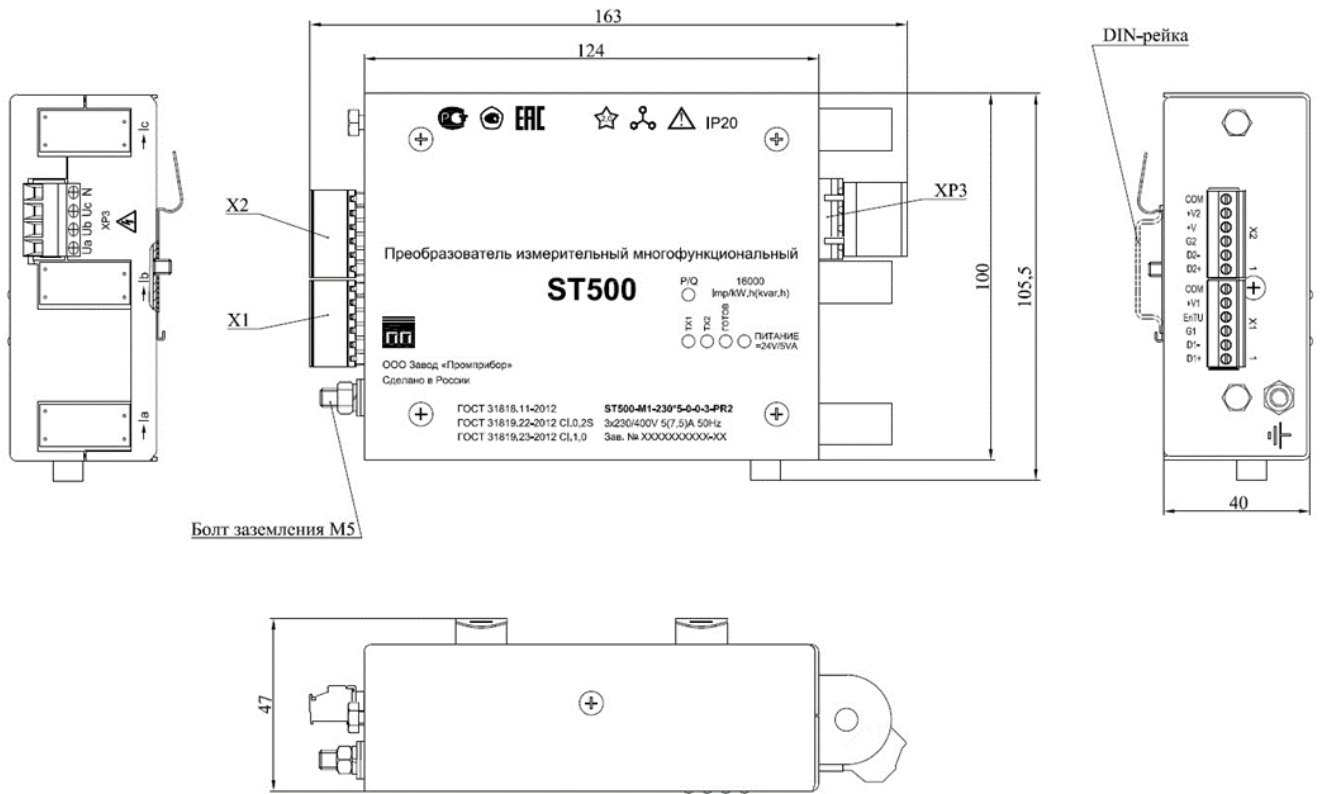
Внешний вид и габаритные размеры МИП ST500-M1-XXX*X-0-0-3-PR2 и ST500-M1.02-XXX*X-0-0-3-PR2
